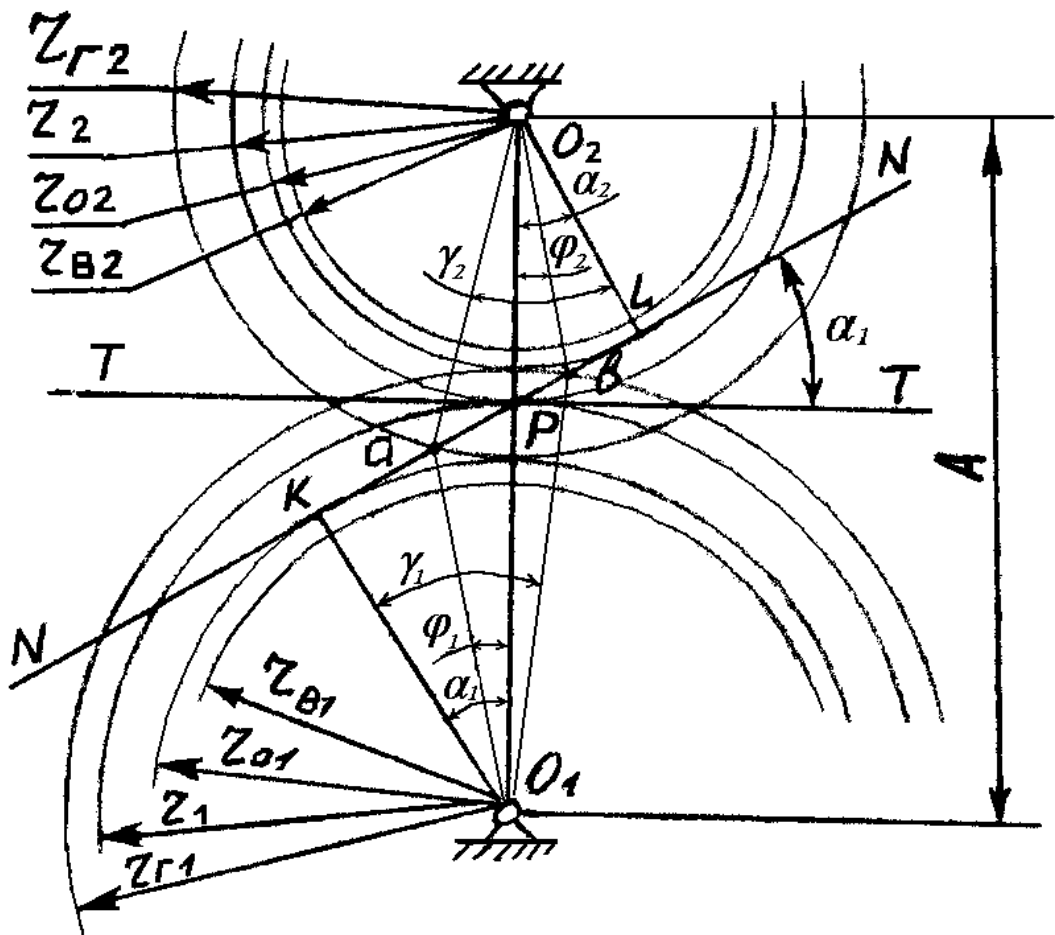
Геометрические параметры зубчатых колес и зацепления
